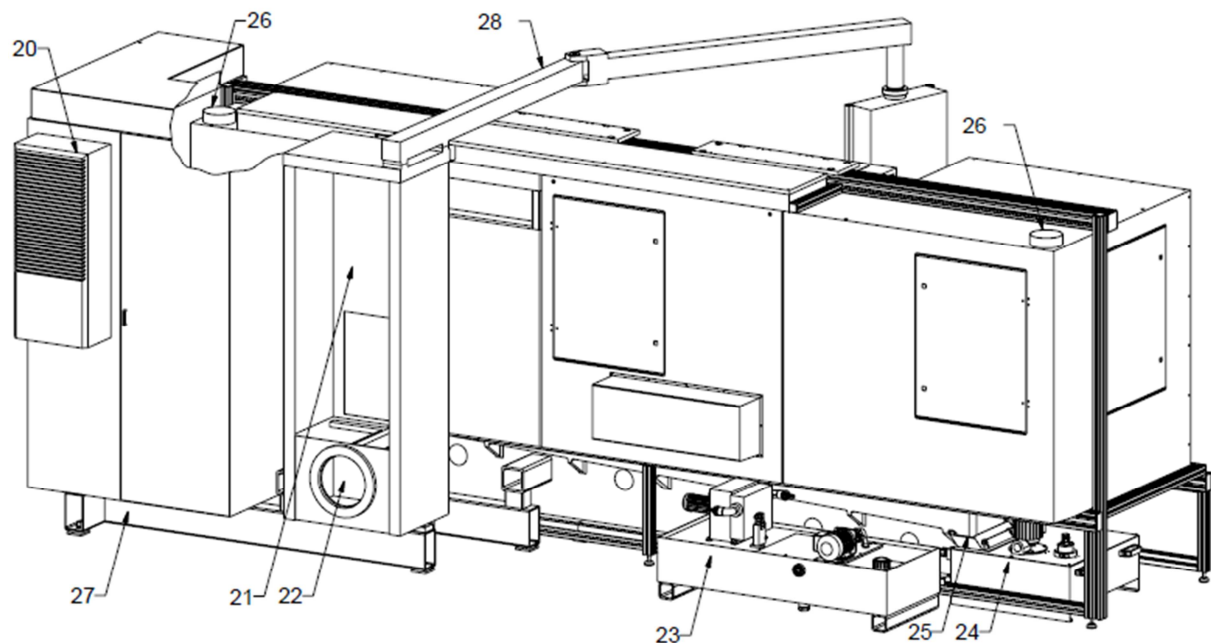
Emplacement des éléments principaux de la vue arrière de la machine.
